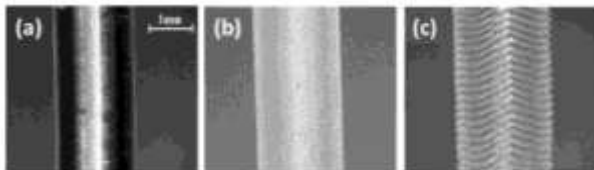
Transición desde un extruido estable hasta la fractura tipo piel de tiburón, (a) superficie brillante, (b) superficie de menor brillo o inicio de la fractura, (c) frac-
